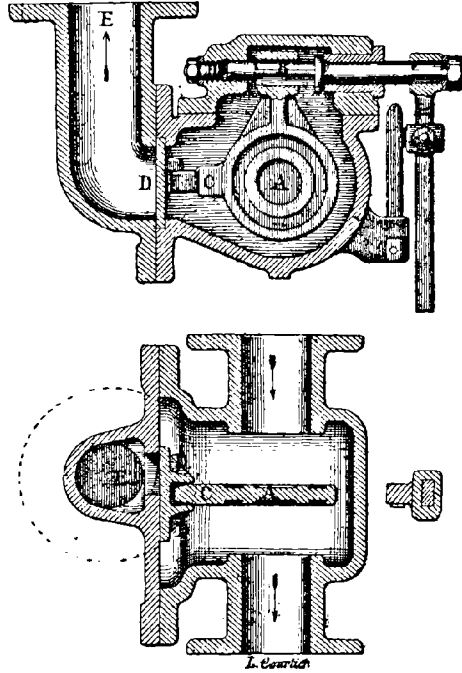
et 728. — Clapet obturateur de vapeur Vaultier (coupe et plan).
